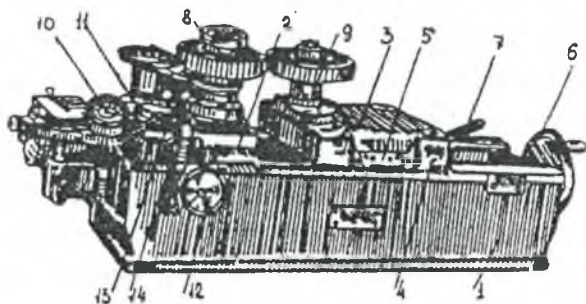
Общий вид межцентромера КПД-300: 1 – основание прибора; 2 – плавающий суппорт; 3 – суппорт; 4 – линейка; 5 – нониус; 6 – маховичок; 7 – зажим; 8 – оправка измерительного колеса; 9 – оправка контролируемого колеса; 12 – рукоятка.
